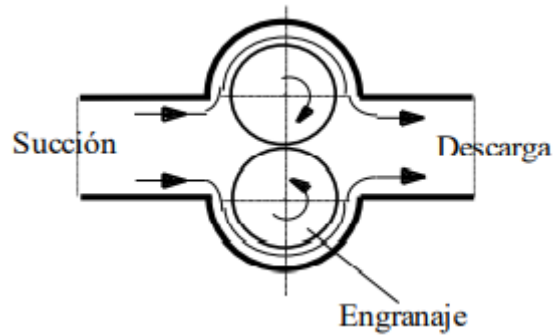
Máquina rotativa de engranajes. Fuente [22]
